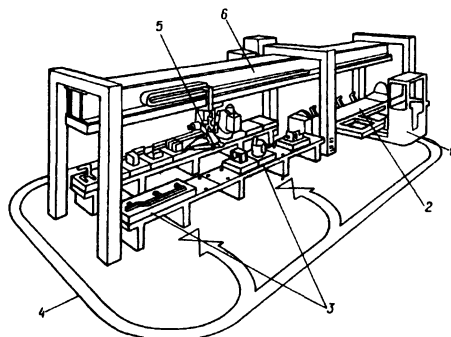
ГПС для дуговой сварки с гибким транспортом:
